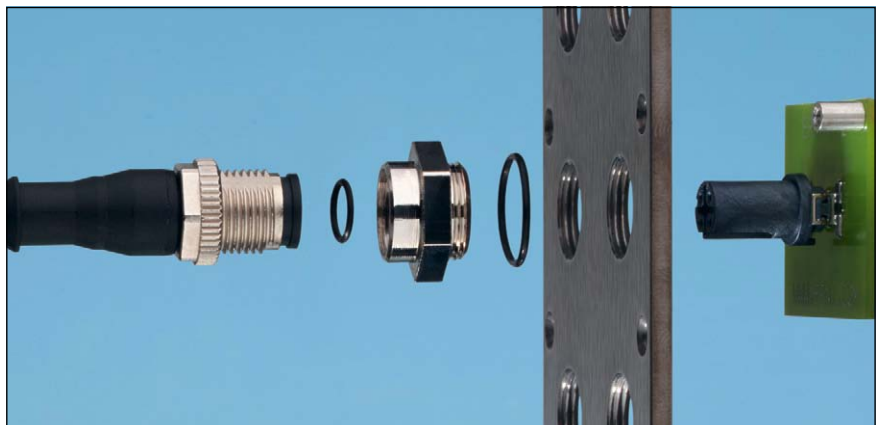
Erni hat ein Baukastensystem für M8/M12-Steckverbinder entwickelt, das besonders flexibel einsetzbar ist. Die Steckverbinder haben so robuste SMT-Anschlüsse, dass sie als Schüttgut verpackt und zugeführt werden können. (Bild: Erni)
